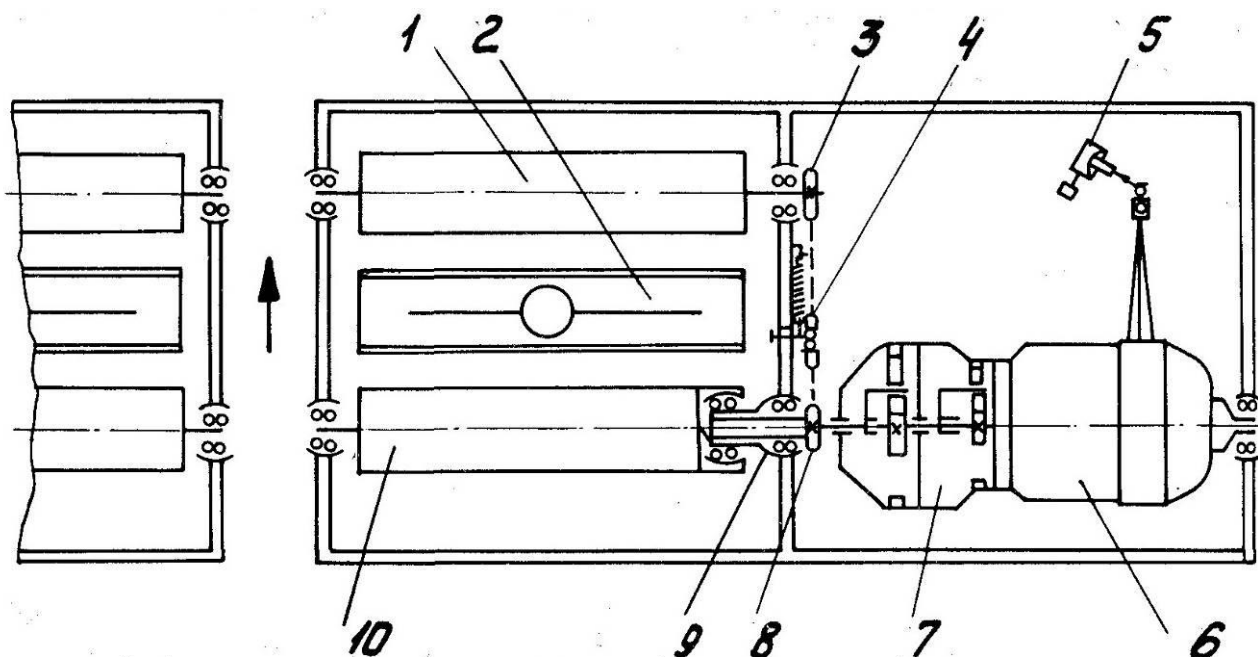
Кинематическая схема опорно-воспринимающего устройства силового тормозного стенда модели К-208М: 1- ведомый беговой ролик, 2 – пневмоподъемник, 3 – ведомая звездочка цепной передачи привода ведомого ролика, 4 – натяжной ролик; 5 - нагрузочное устройство системы замеров; 6 – электродвигатель; 7 – планетарный редуктор (двухступенчатый); 8 – ведущая звездочка; 9 – втулочно-пальцевая муфта; 10 – ведущий беговой ролик
